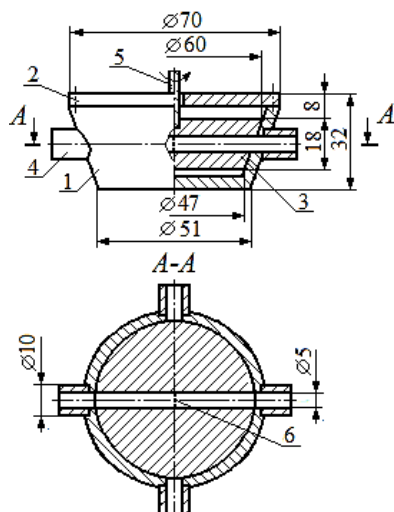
Схема дозатора ионита (повернуто): 1 – корпус; 2 – крышка; 3 – пробка; 4 – штуцер; 5 – вал; 6 – сетка
